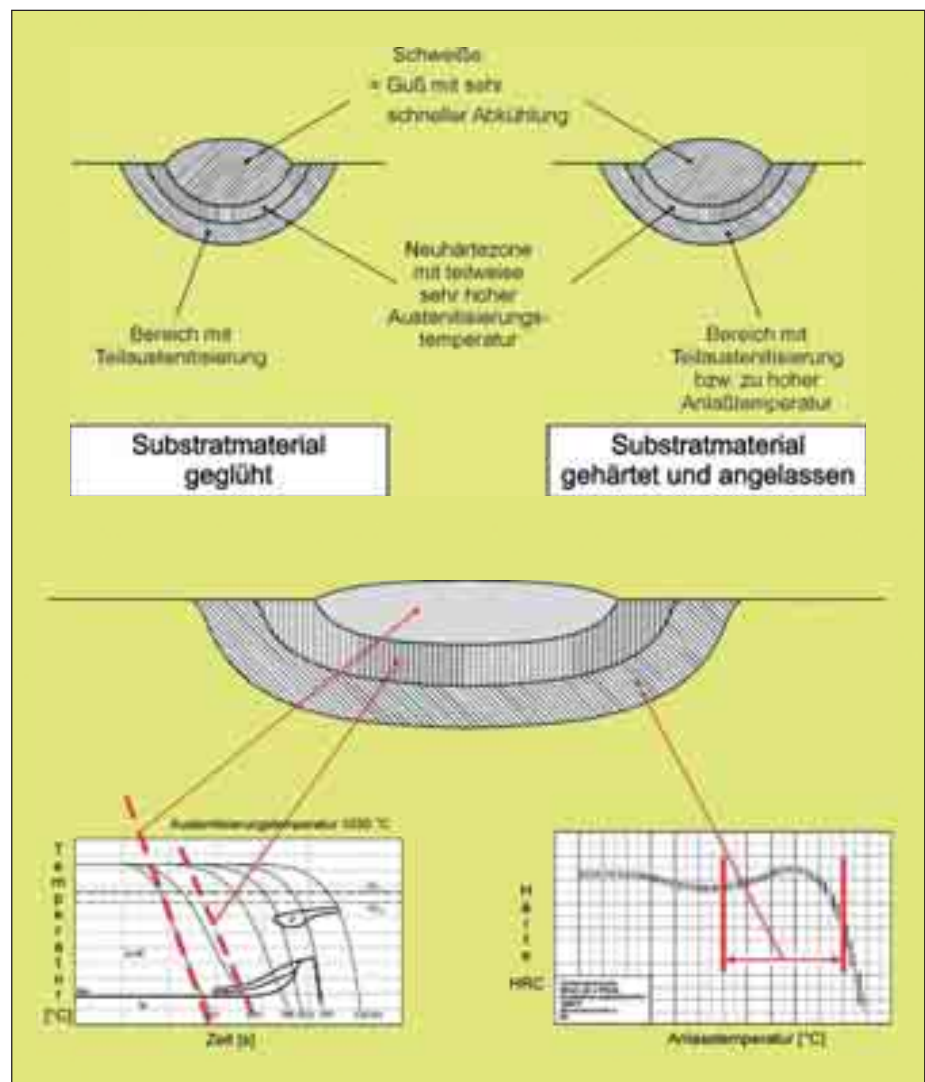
Schweißnahtausbildung bei Werkzeugstählen im geglähten und angelassenen Zustand (oben)
